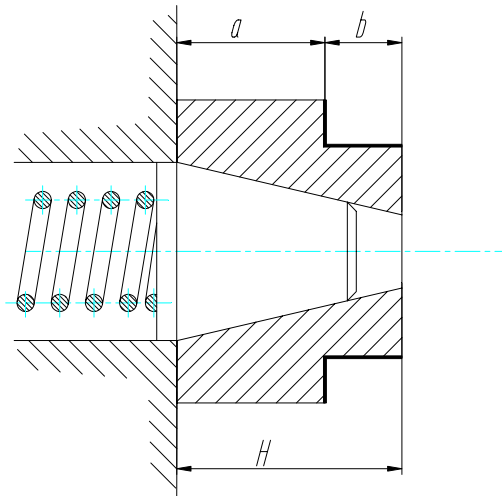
Схема усовершенствованного токарного приспособления с базированием заготовки по конусу.
